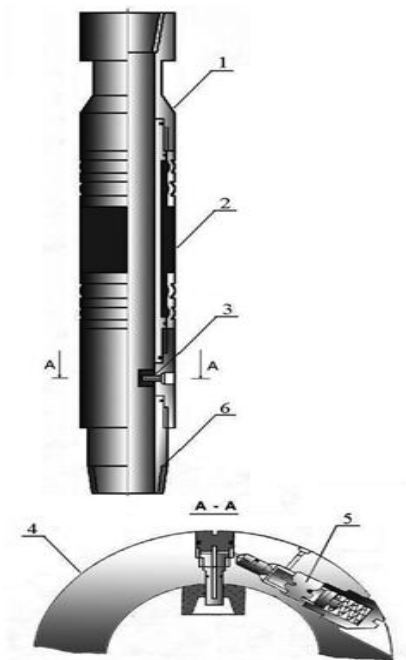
Основные элементы Пакера ПГПМ1: 1 - верхний переводник; 2 - резиноканальный уплотнительный элемент; 3 - узел защиты пакера от преждевременного срабатывания; 4 - корпус клапанного узла; 5 - клапанный узел пакера; 6 - нижний переводник.
